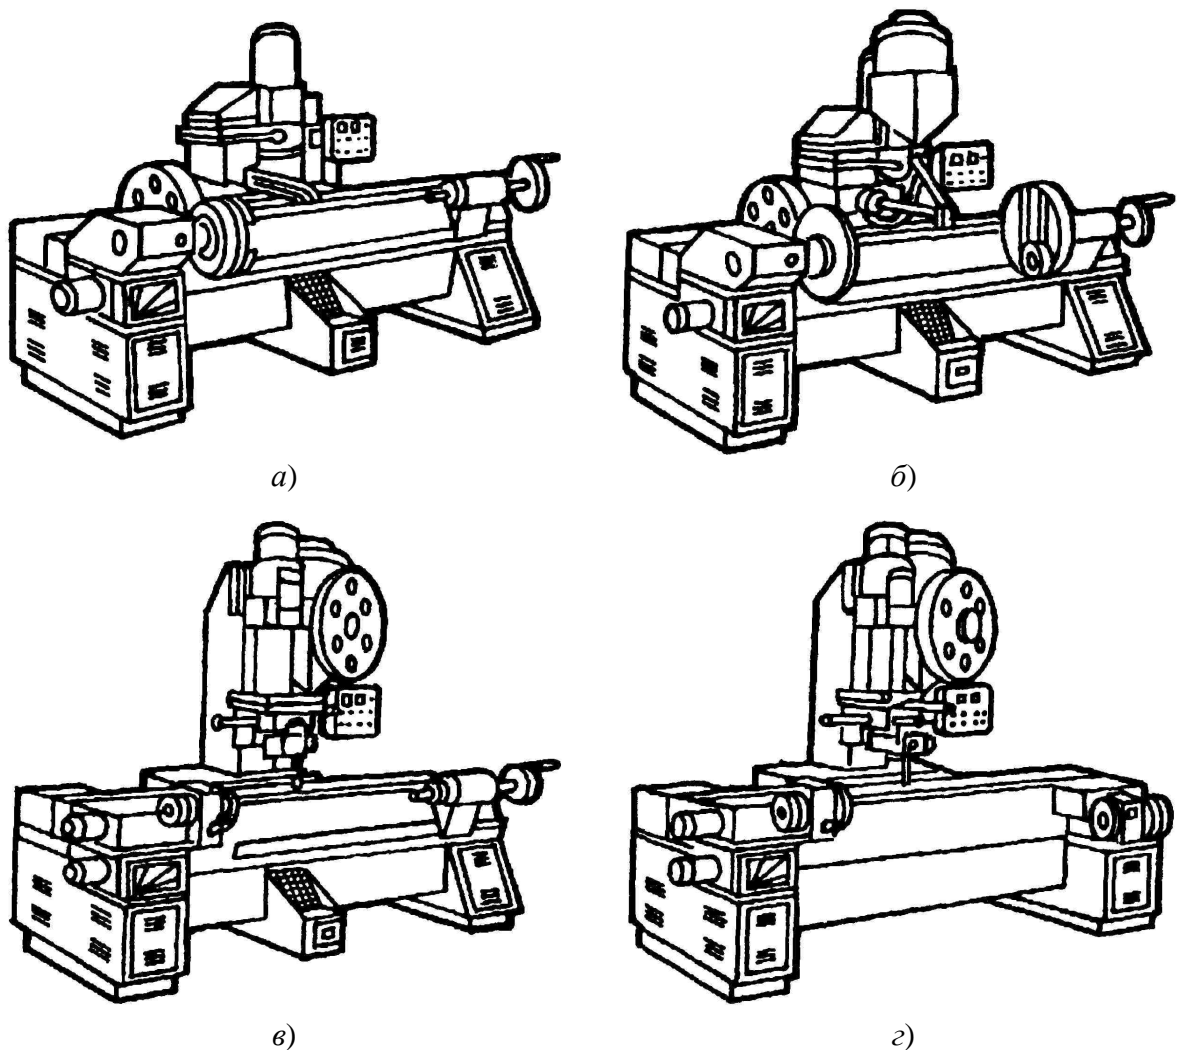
Компонировочные схемы станков для электродуговой наплавки деталей: *а* – станок У-651 для наплавки валов; *б* – станок У-652 для наплавки коленчатых валов; *в* – универсальный наплавочный станок У-653; *г* – наплавочный универсальный двухпозиционный станок У-654
